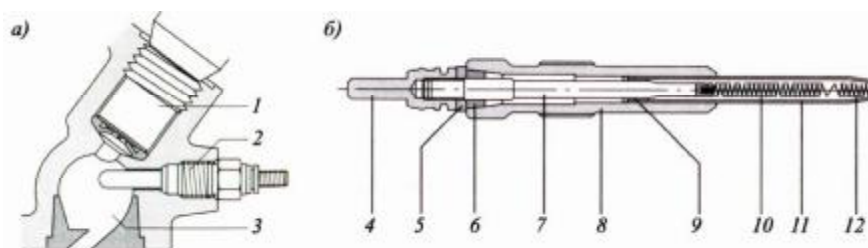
Розташування свічки розжарювання у вихровій камері згоряння (а) та будова штифтової свічки (б): 1 – форсунка; 2 – свічка розжарювання; 3 – камера згоряння; 4 – наконечник; 5 – ізоляційна прокладка; 6 – подвійне ущільнення; 7 – стрижень; 8 – корпус; 9 – ущільнення захисної оболонки; 10 – нагрівальна спіраль; 11 – оболонка; 12 – порошок
